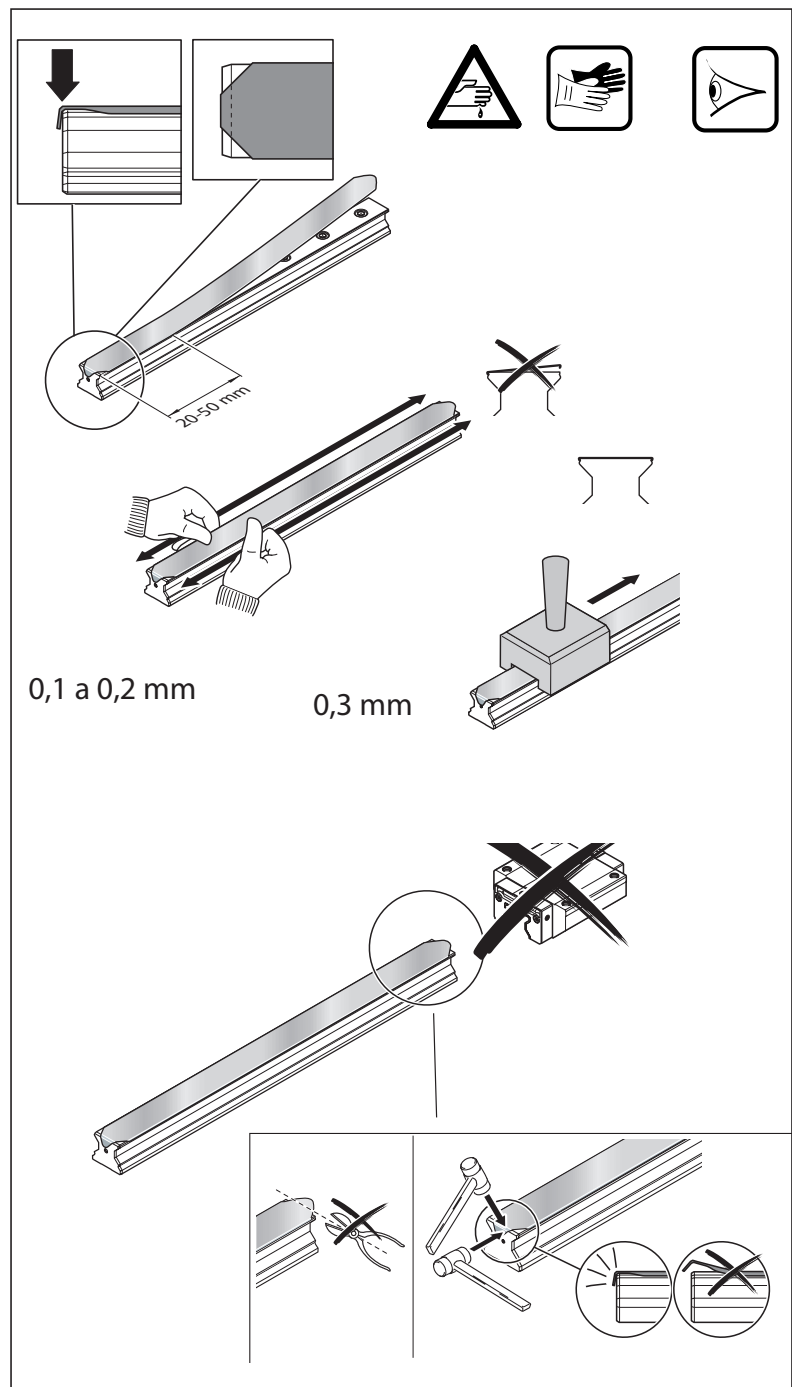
Montaje de bandas de protección con la longitud adecuada de la banda de protección
